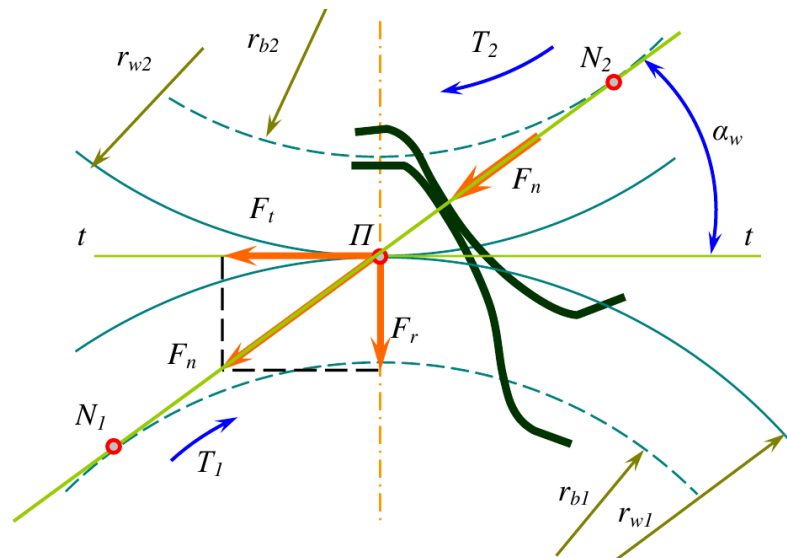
Схема сил у зачепленні прямозубої циліндричної передачі
